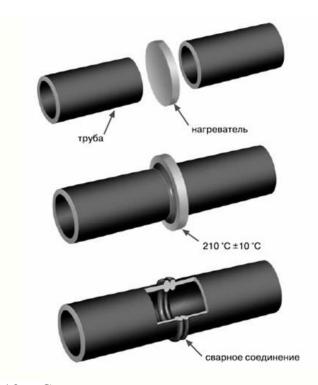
Схема стыковой сварки полиэтиленовых труб
